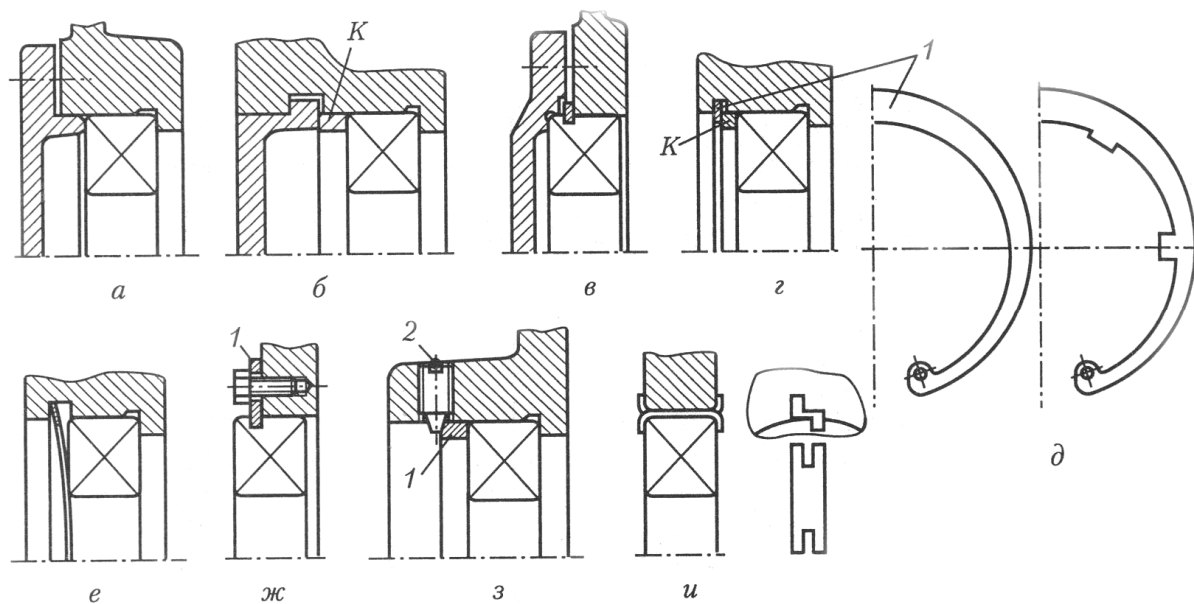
Способы крепления подшипников качения в корпусе:
